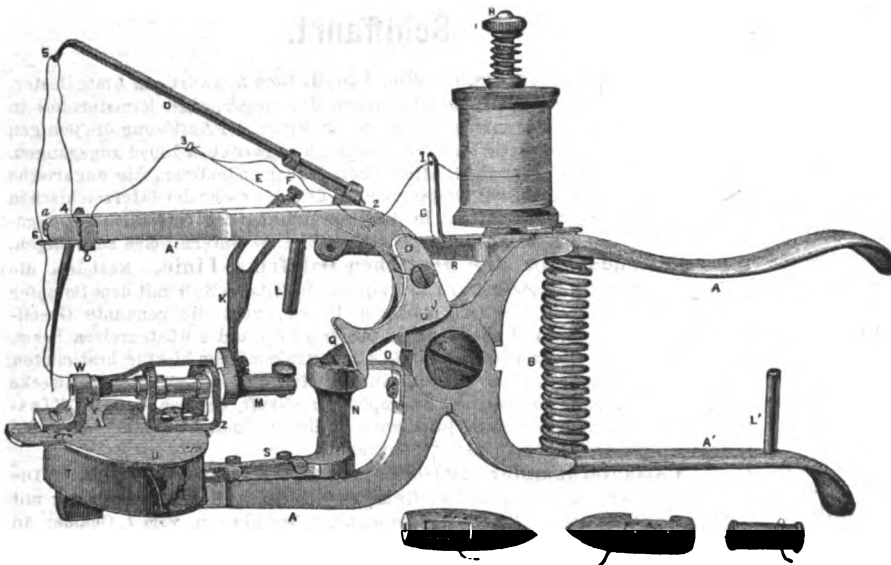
Hand-Nähmaschine von der Hand Sewing Machine Company, Bridgeport (Connecticut).
